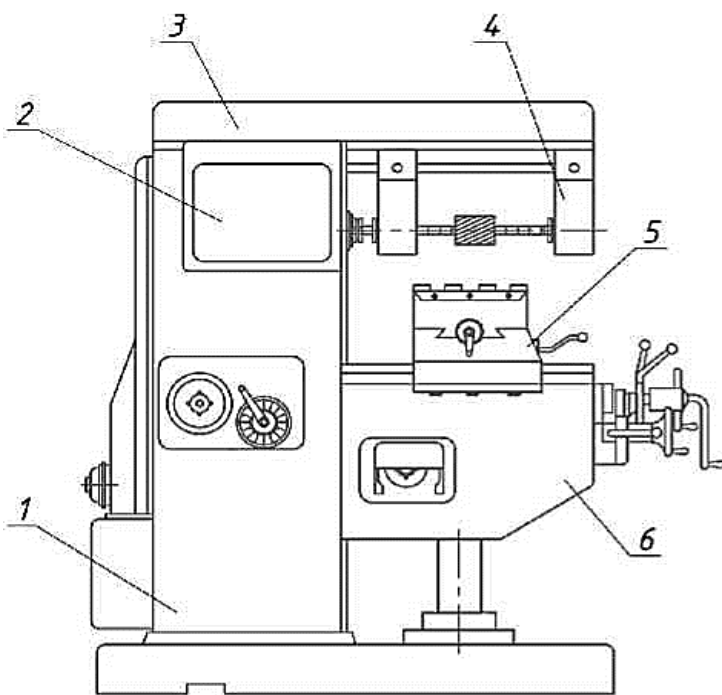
Загальний вигляд горизонтально-фрезерного верстата
